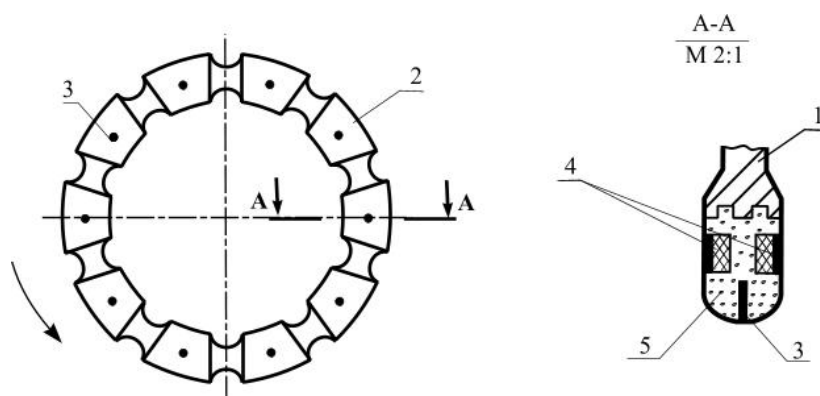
Схема оснащения рабочего торца опытной коронки типа БТ20 вставками АПКМ диаметрами 1,3, 1,9 мм или вставками твесала размером 3×4 мм: 1 – корпус коронки; 2 – алмазосодержащая матрица; 3 – вставки АПКМ или вставки твесала; 4 – подрезные вставки твесала; 5 – алмазы
